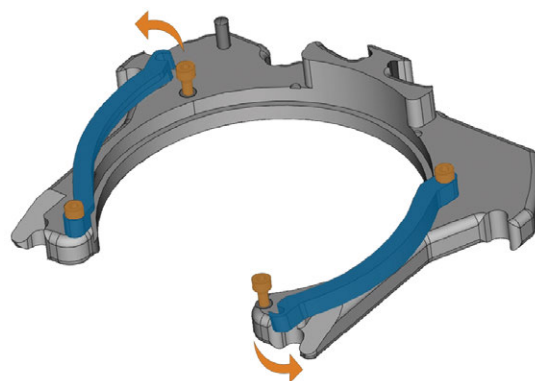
OUVERTURE DES CROCHETS DE FIXATION DU CADRE DE PIÈCES BRUTES
